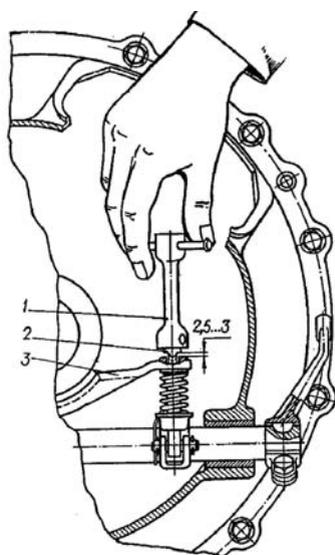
Регулировка тормозка: 1 — ключ; 2 — гайка; 3 — тормозная колодка
